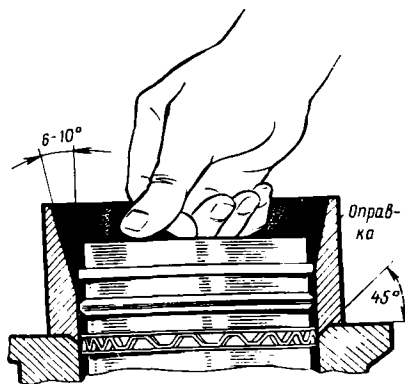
Установка в цилиндр поршня со стальными кольцами с помощью оправки
